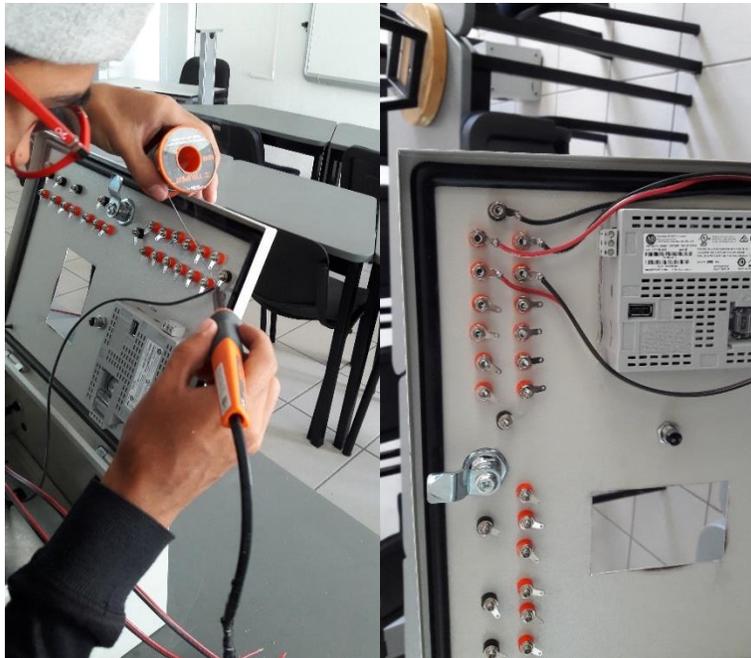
Proceso de soldadura de los cables para las entradas del PLC del gabinete.
